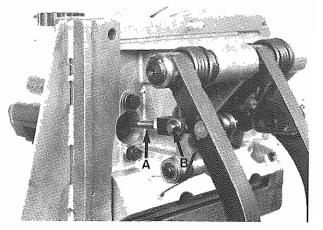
A - Puntalino - Adjusting rod B - Copiglia - Clip
